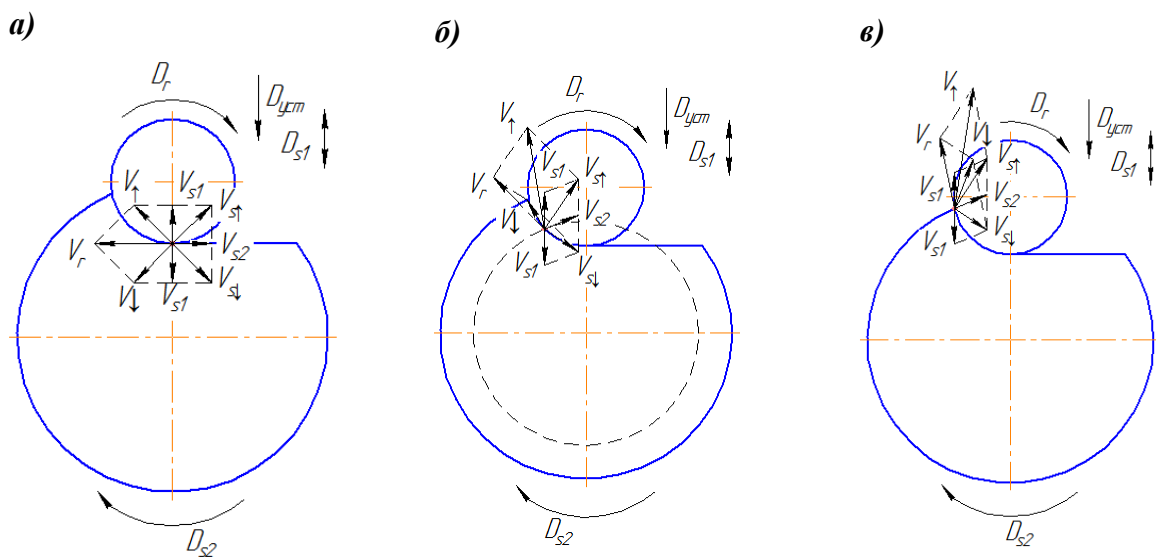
Направления линейных скоростей резания при встречном фрезеровании плоской поверхности: а) в точке врезания инструмента в заготовку, б) в середине участка обработки, в) в точке выхода инструмента из заготовки
